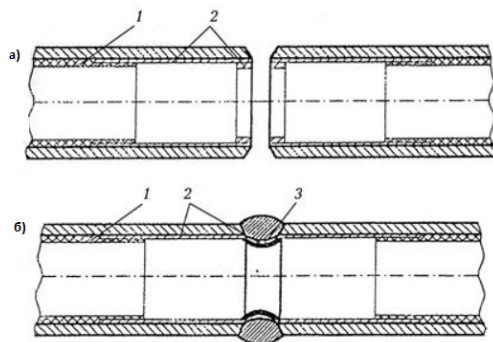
Конструкция внутреннего полимерного покрытия труб с металлизацией концевых участков нержавеющей сталью: а – до сварки; б – после сварки; 1 – полимерное покрытие; 2 – металлизационное покрытие; 3 – слой сварочных шлаков
